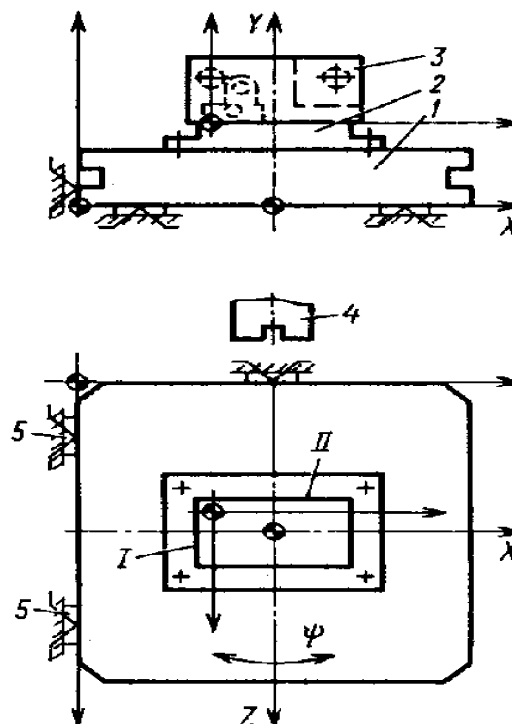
Установка заготовки на супутнику при обробці на багатопільовому верстаті 6904ВМФ1
